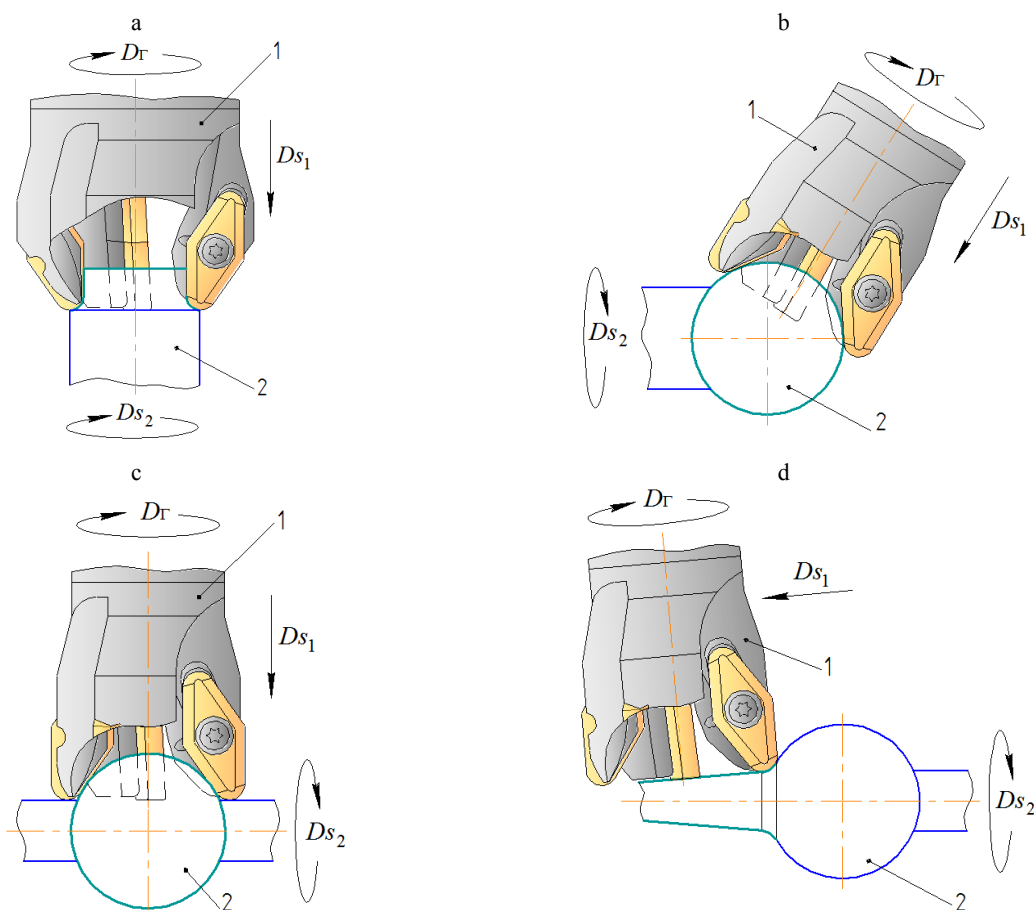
Схемы обработки охватывающими фрезами (зенкерами) поверхностей:
